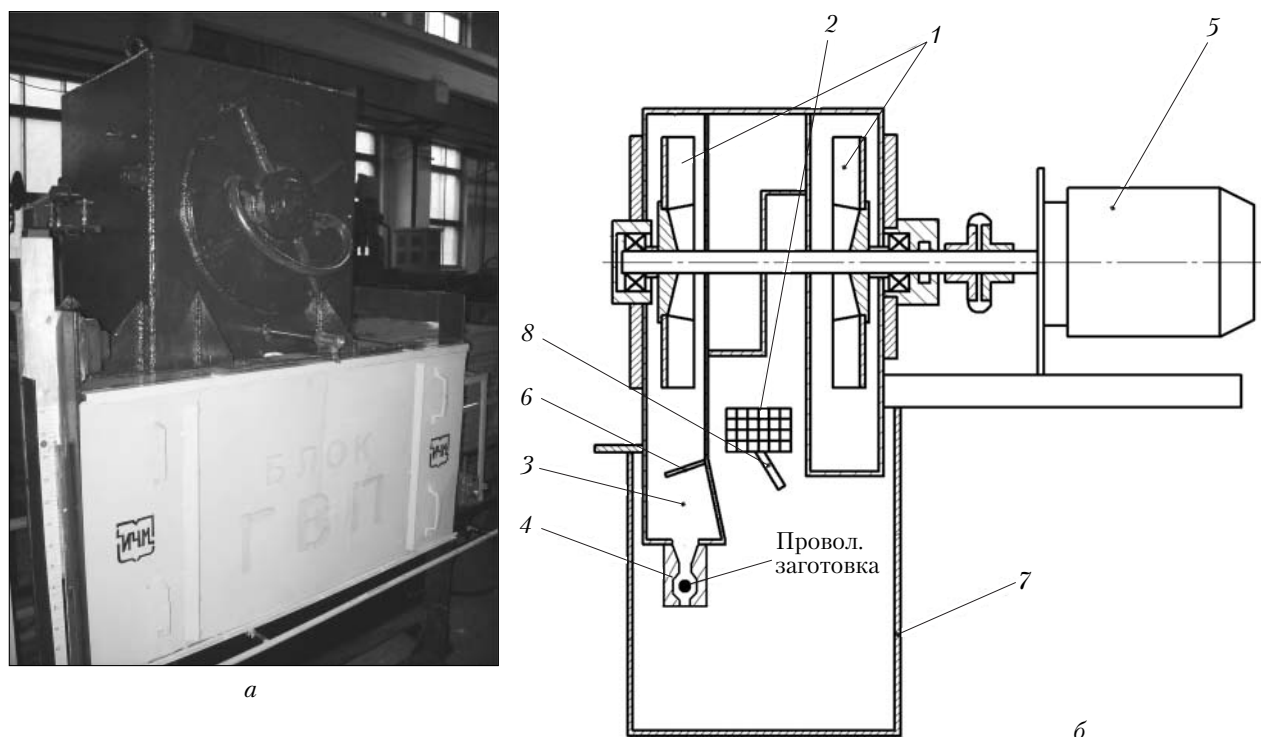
Внешний вид (а) и схема конструкции (б) блока струйного охлаждения
